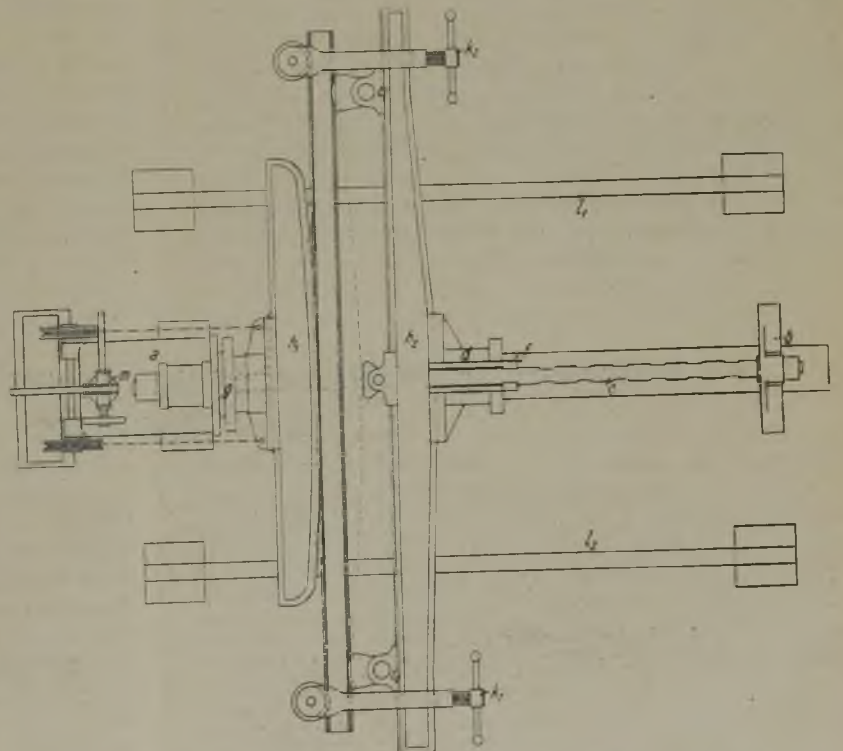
Ansicht der hydraulischen Biegemaschine von oben.
